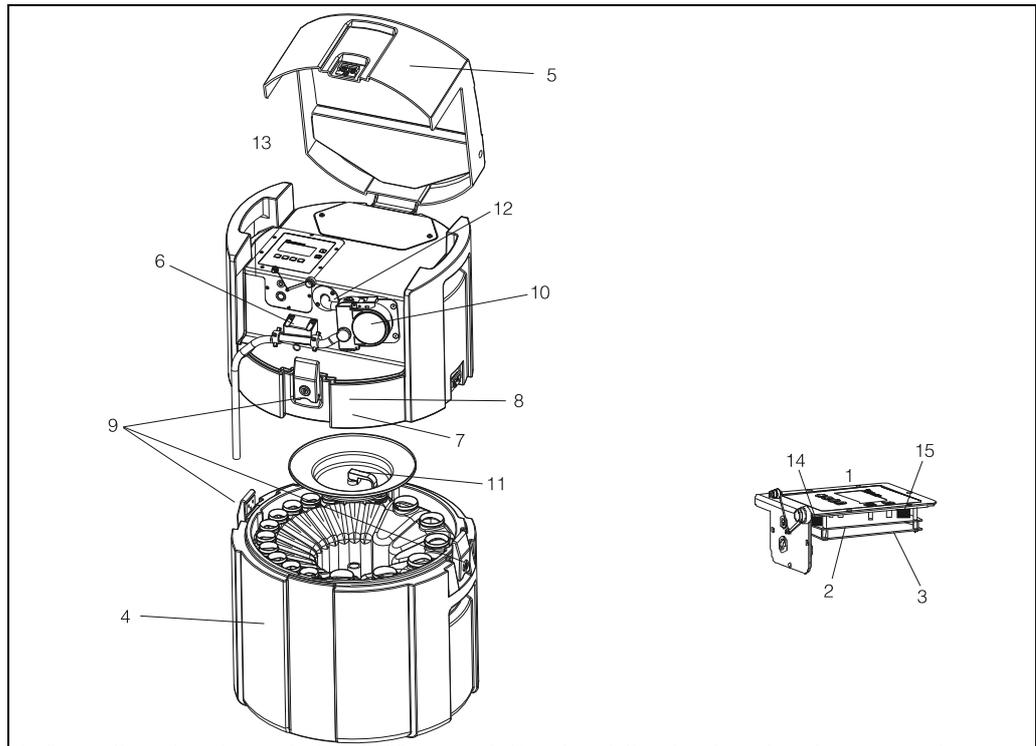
Pièces de rechange Liquiport 2000 Ex (pour la légende, voir liste des pièces de rechange page suivante)
